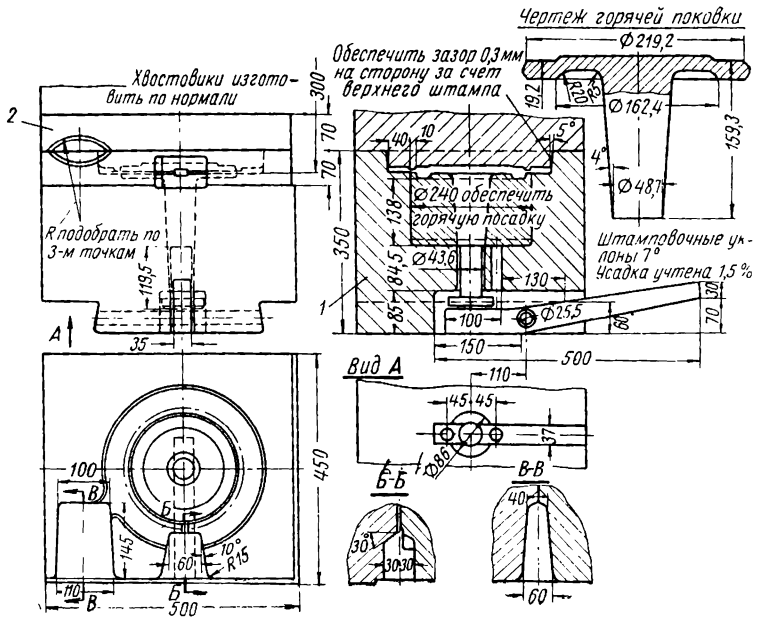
Молотовый штамп для поковки оси переднего колеса трактора
